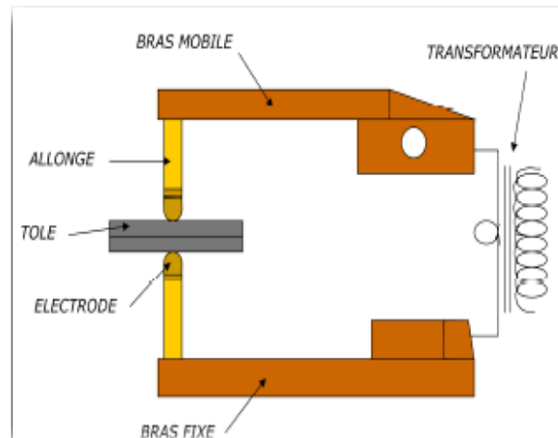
Mécanisme du soudage par point [21].
